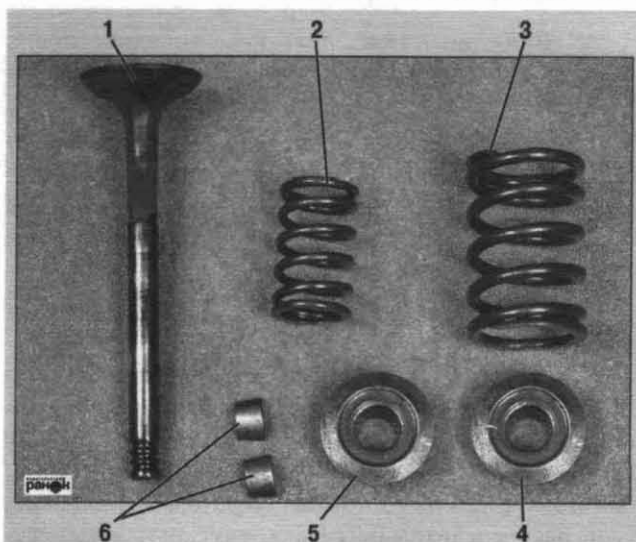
Клапан и его детали: 1 — клапан; 2 — внутренняя пружина клапана; 3 — наружная пружина клапана; 4 — тарелка пружины клапана; 5 — шайба опоры пружины; 6 — сухари клапана
